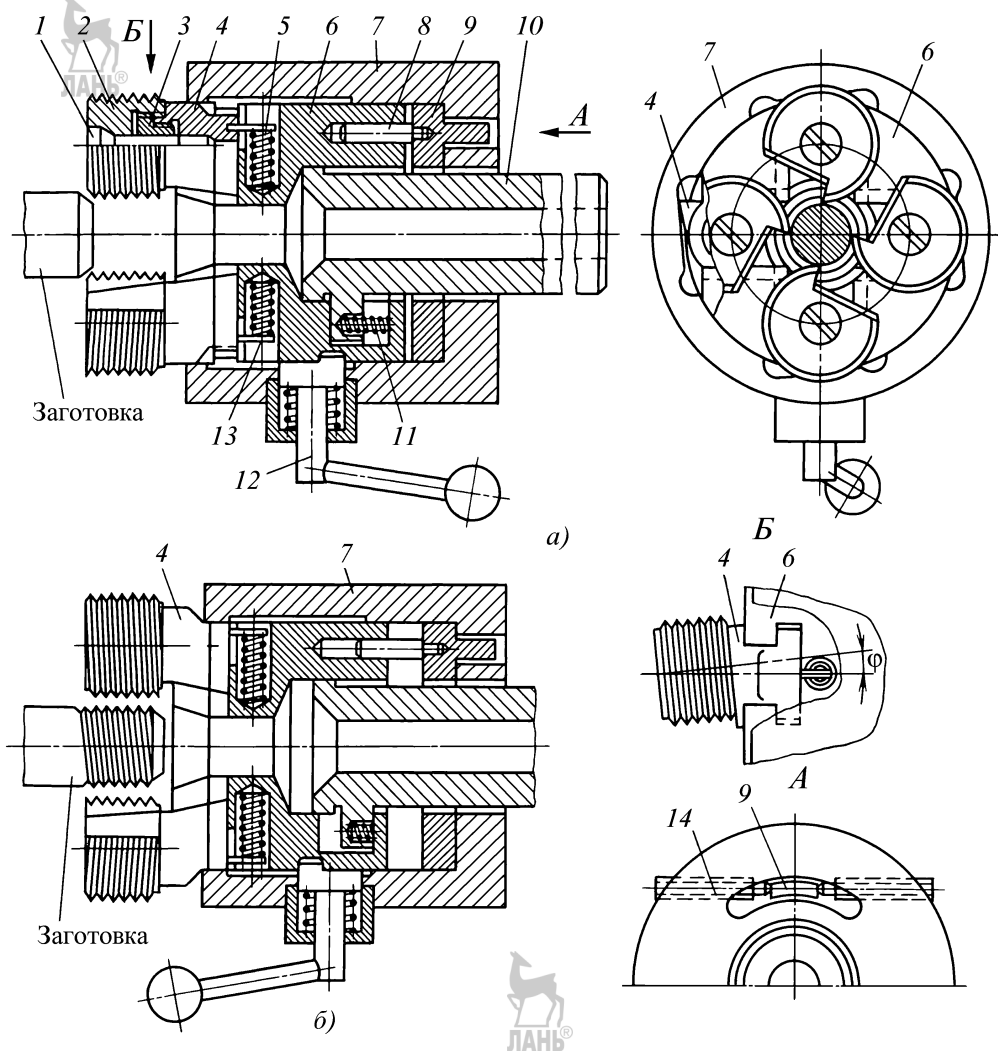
Невращающаяся винторезная головка для нарезания наружной резьбы в рабочем (а) положении и с открытыми гребенками (б):
